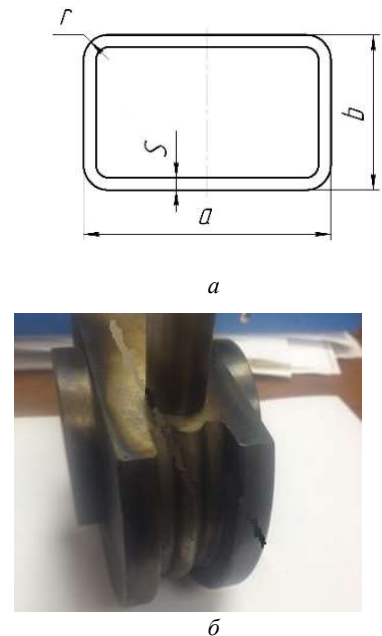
Размеры профиля заготовки и общий вид фасонного валака:
